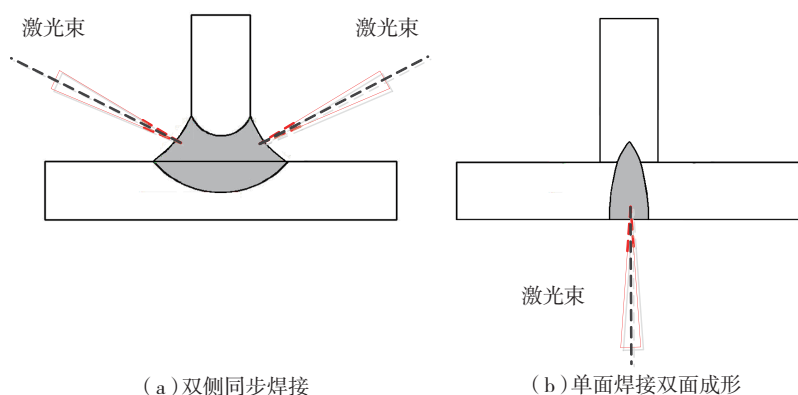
双侧同步焊接与单面焊接双面成形工艺
